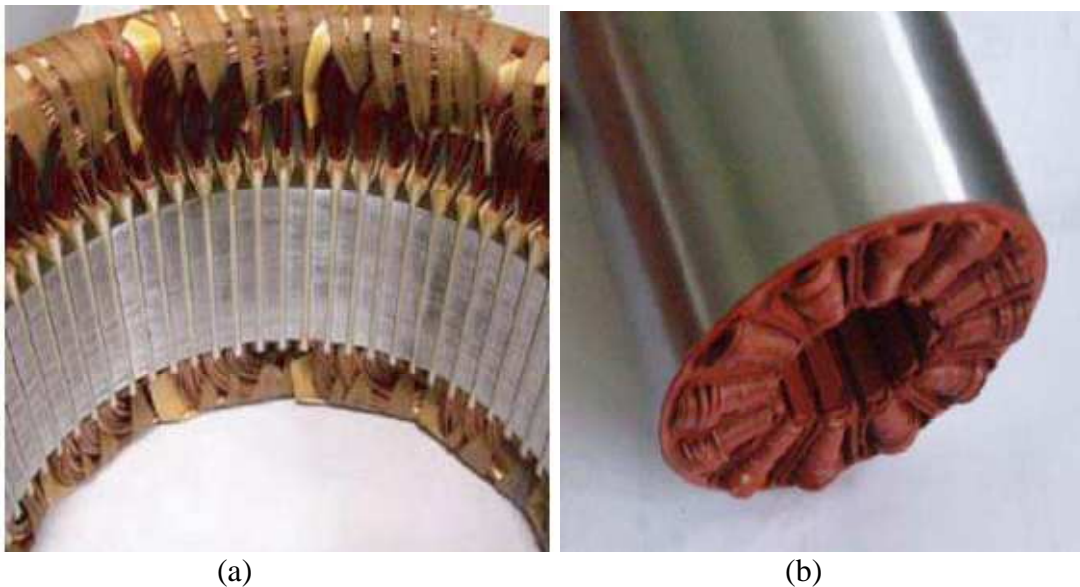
Exemples de type de bobinage ; (a) régulier, (b) non régulier [2].
